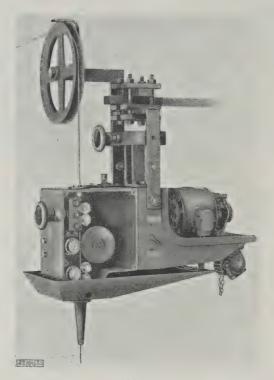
Schweißkopf des Lichtbogen-Schweißautomaten der Siemens-Schuckertwerke, geöffnet.
